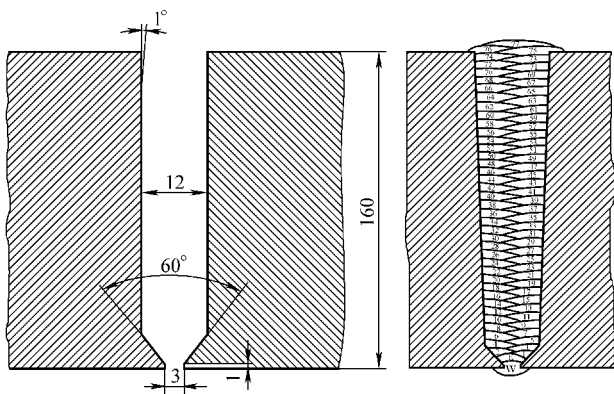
窄间隙埋弧焊焊件的实际坡口与焊道设计尺寸
